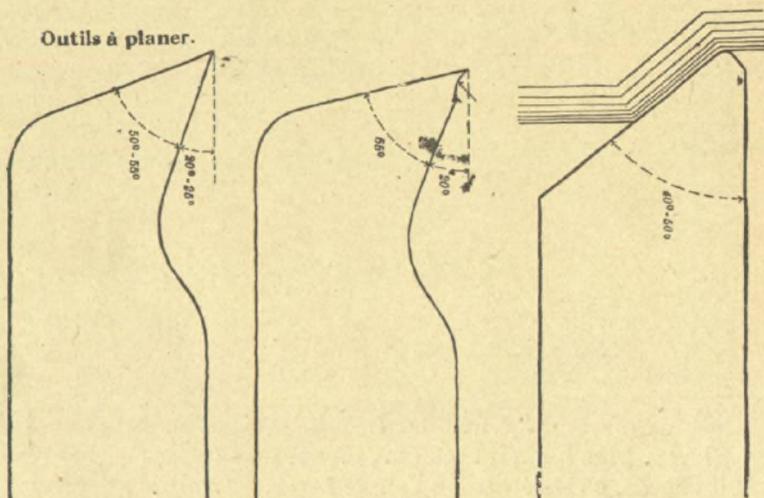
Outils pour terminer. Ils ont la même forme tant pour les pièces lourdes que pour les pièces légères.
